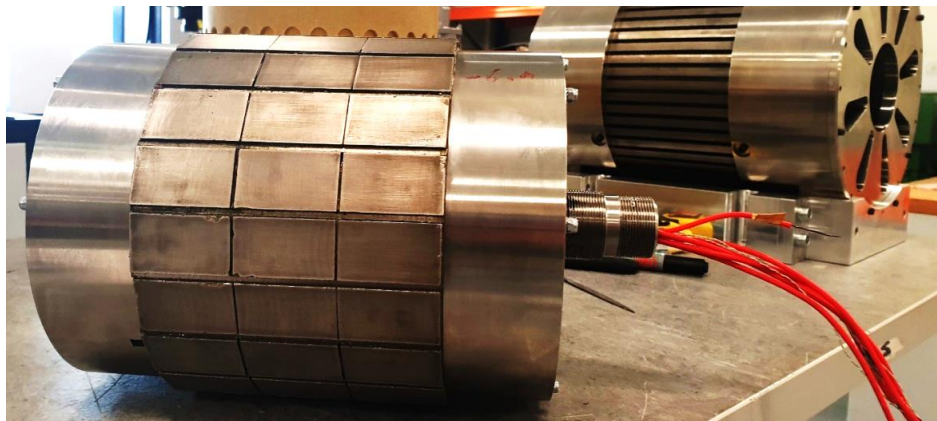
Assemblage du rotor haute vitesse et du stator.
